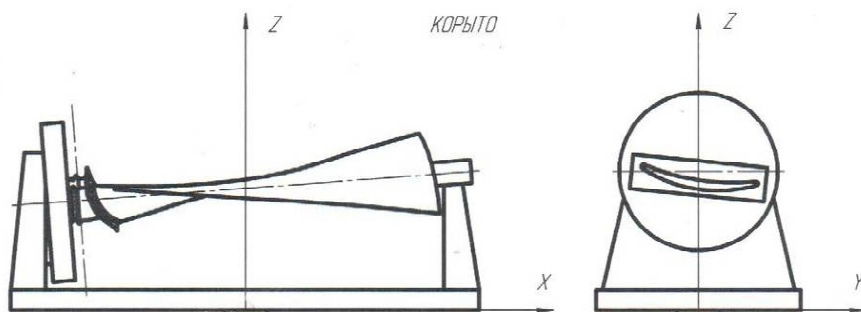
Установка заготовки на станок с ЧПУ ФП-17
